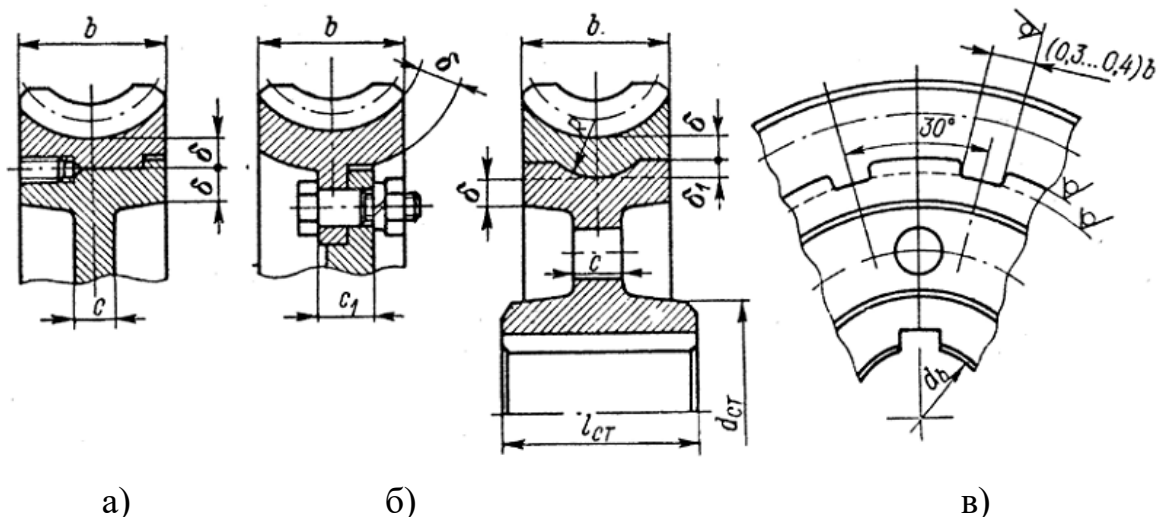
Конструкции и ориентировочные размеры червячных колес со штампованной или кованой ступицей: а – бронзовый венец закреплен винтами; б – венец закреплен болтами; в – залит на ступицу, на ободке которой есть углубления.
